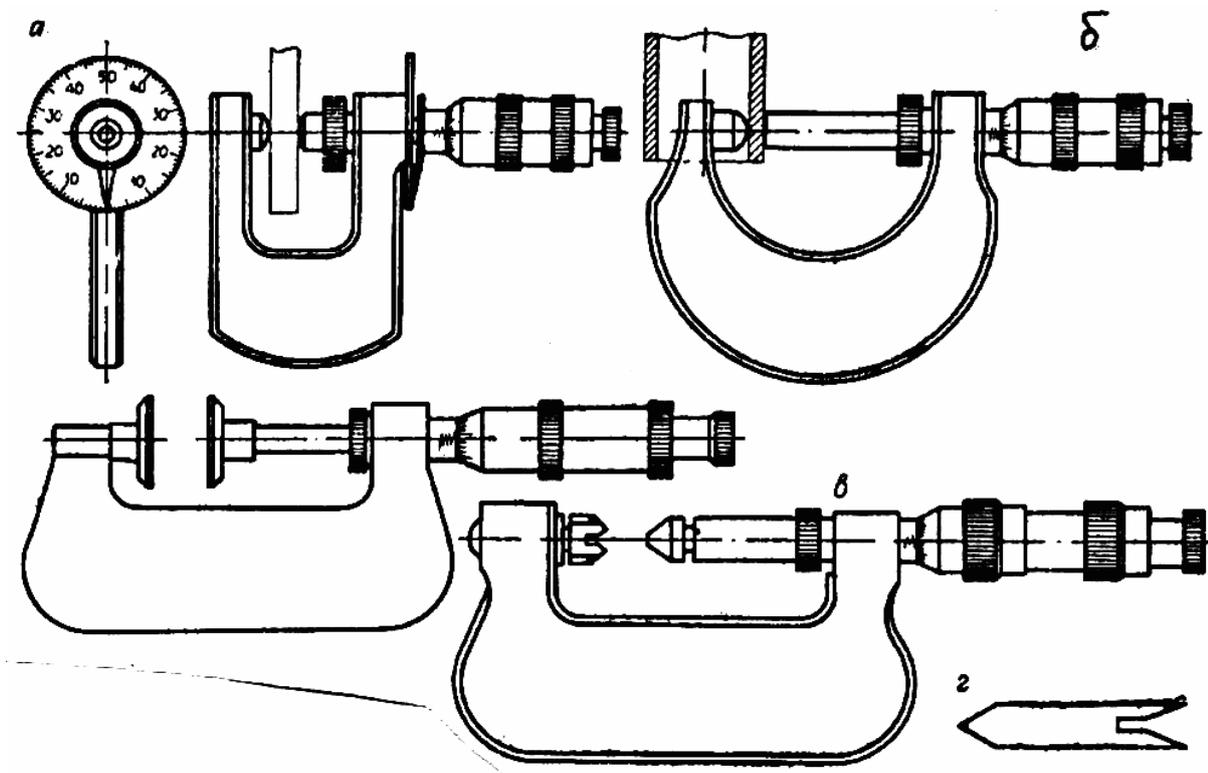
Специальные микрометры: а – листовый; б – трубный; в – зубомерный; г – резьбомерный
